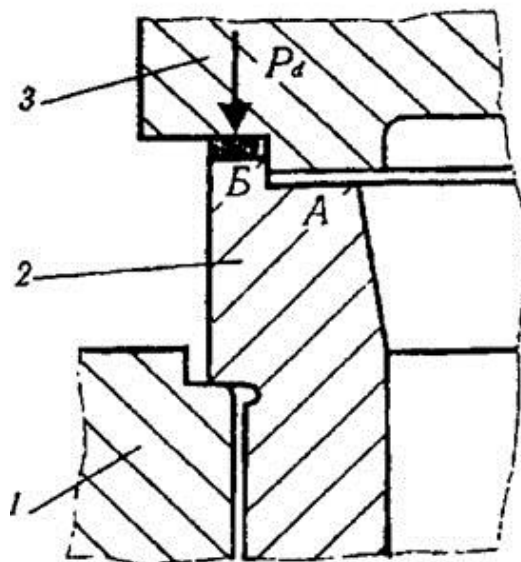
Конструкция узла «блок цилиндра - втулка - крышка цилиндра»:
